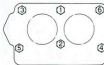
Smontaggio del motore: schema dell'ordine di serraggio delle viti di flangia testa cilindri.
